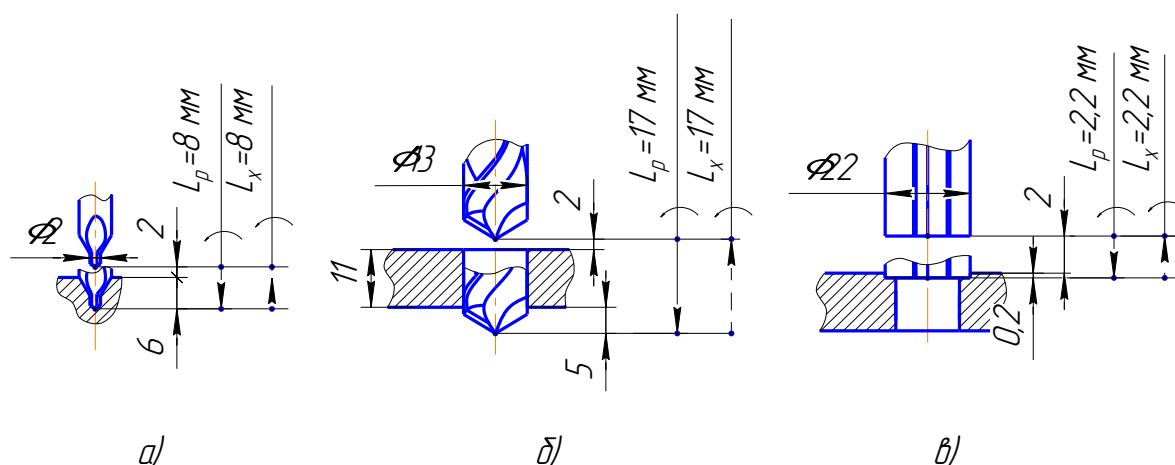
Налагодження інструмента: а) центрування; б) свердлення; в) торцювання.
